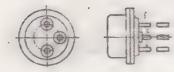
Общий вид и схема расположения выводок: 1 — эмиттер; 2 — коллектор; 3 — база
